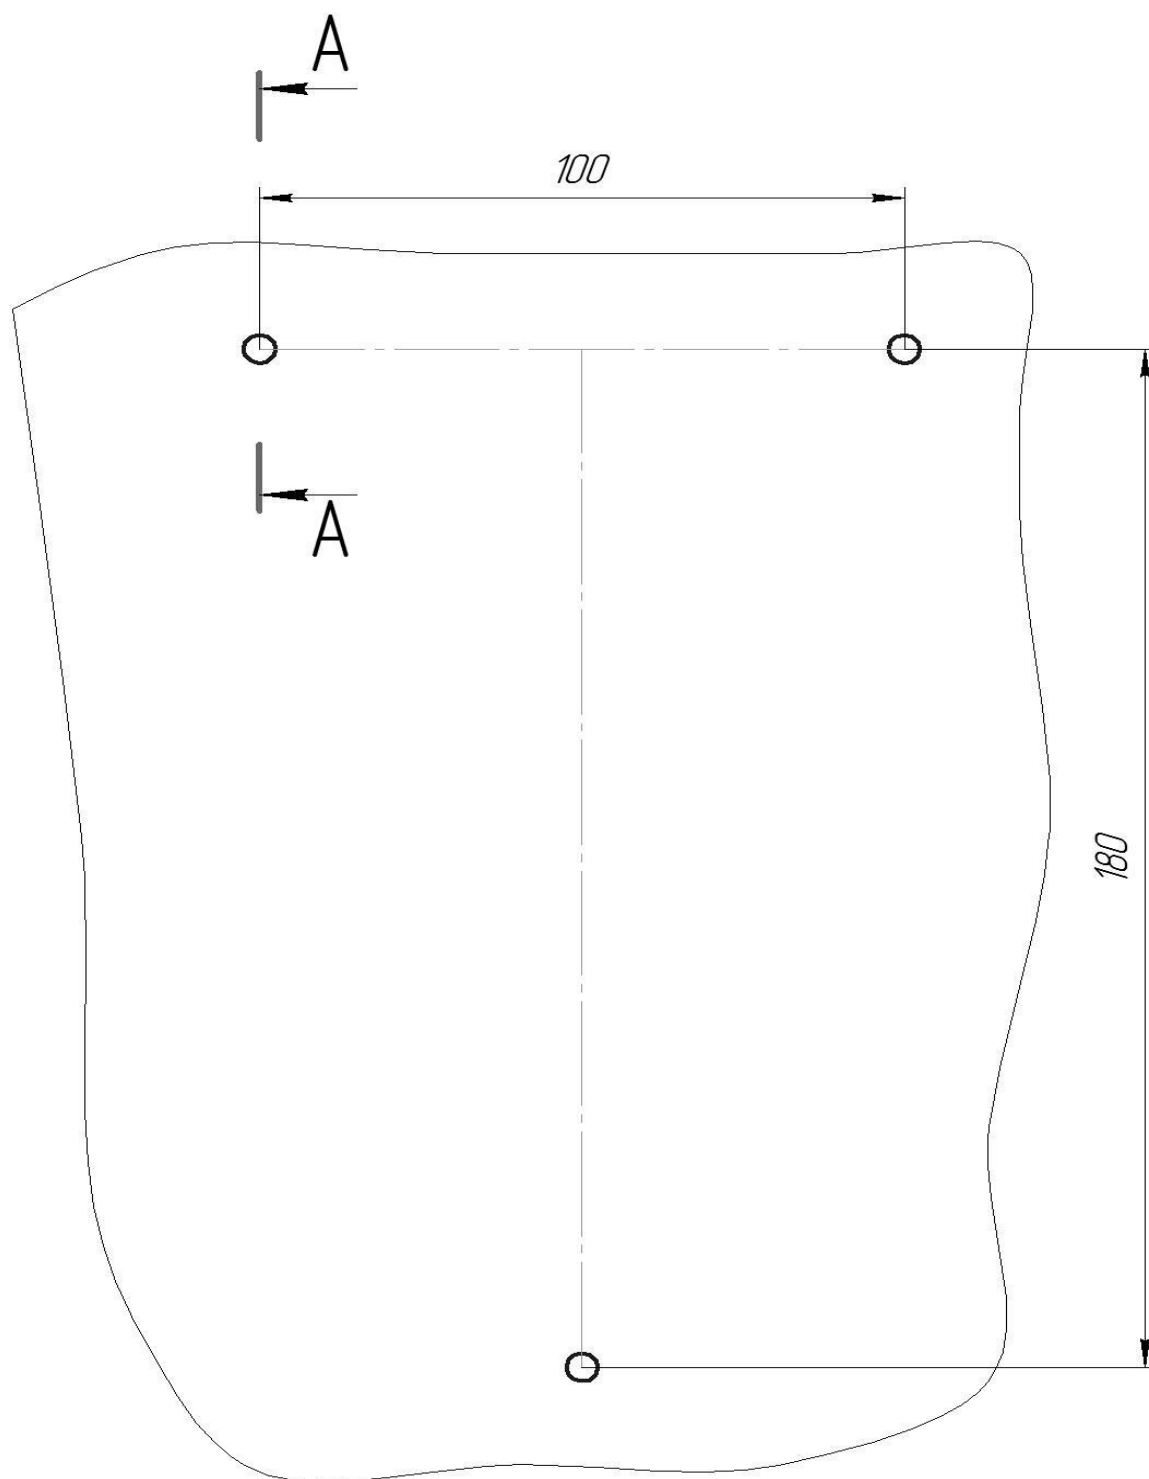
Разметка отверстий для крепления блока ПУИ-32М
